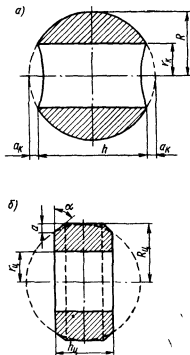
Формы роторов: а — облегченный шаровой ротор; б — цилиндрический ротор со скосами
